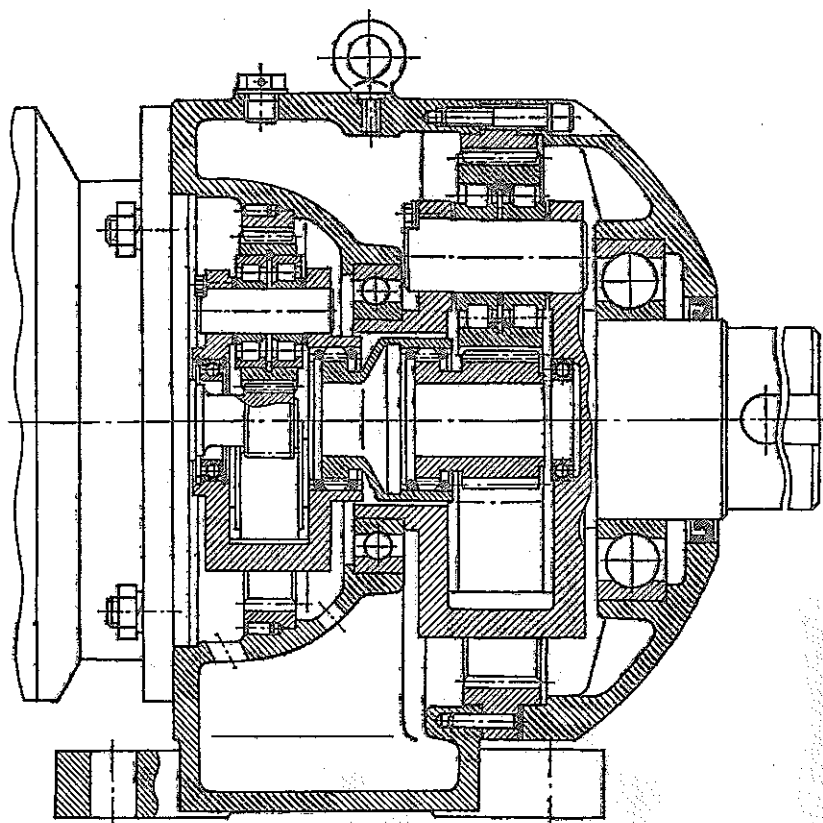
Планетарный двухступенчатый мотор-редуктор
